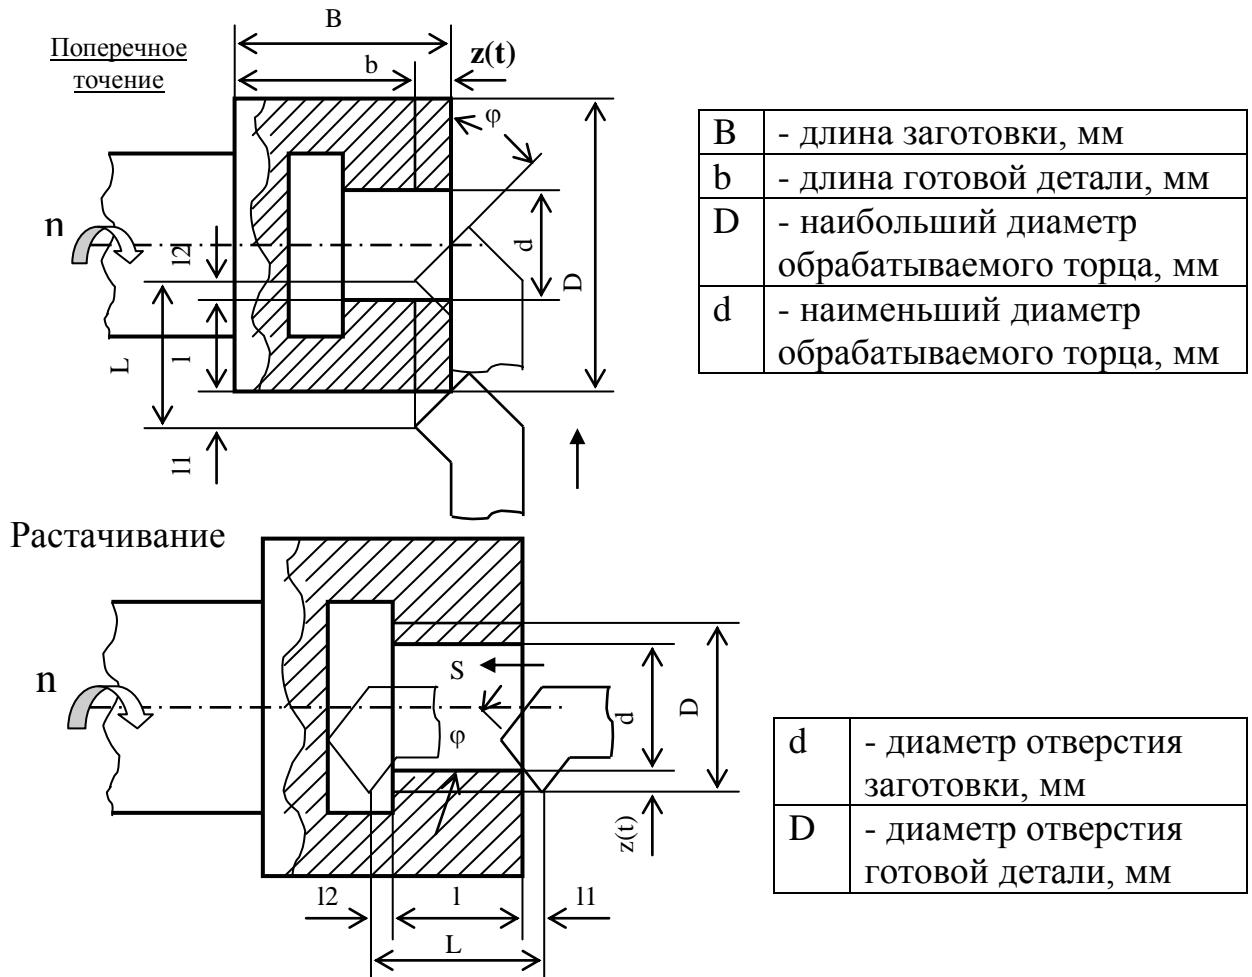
Схемы обработки наружных, торцевых и внутренних поверхностей
